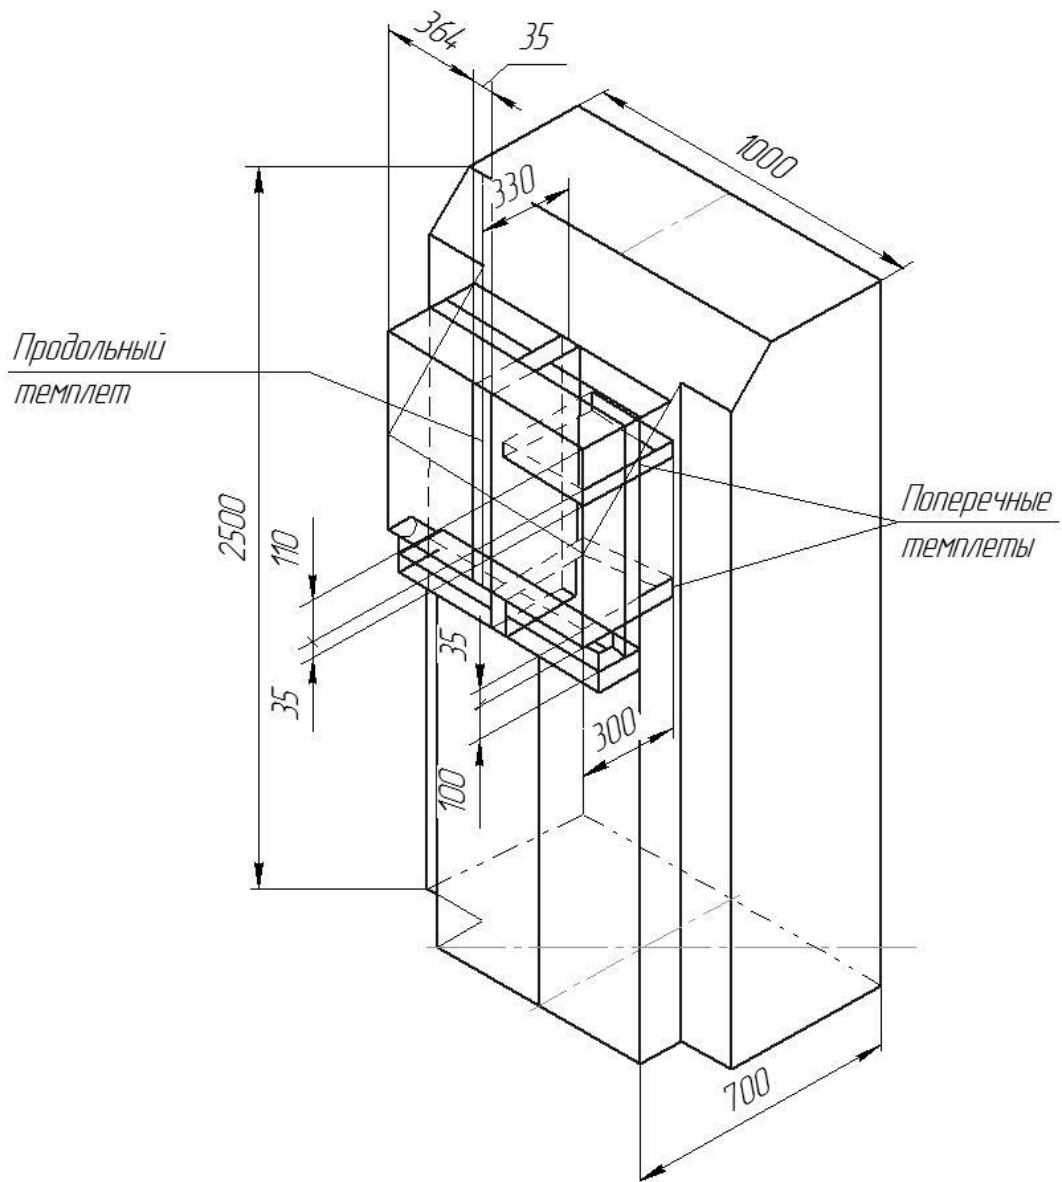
Схема вырезки темплетов из сварного соединения образца
